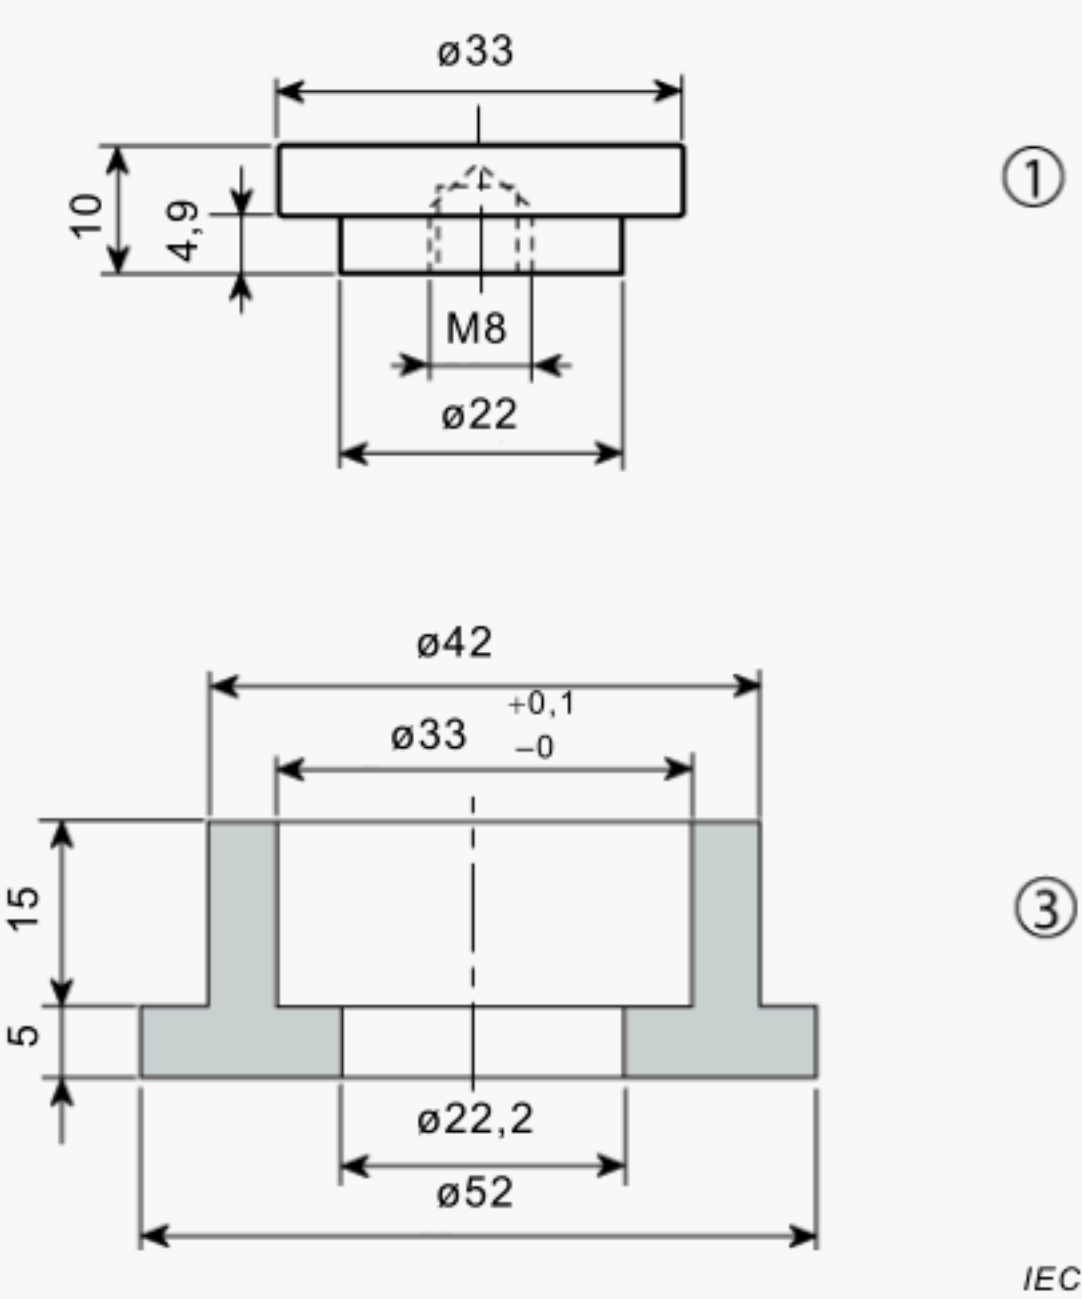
Pour tube rempli de mousse de 32 mm de diamètre
